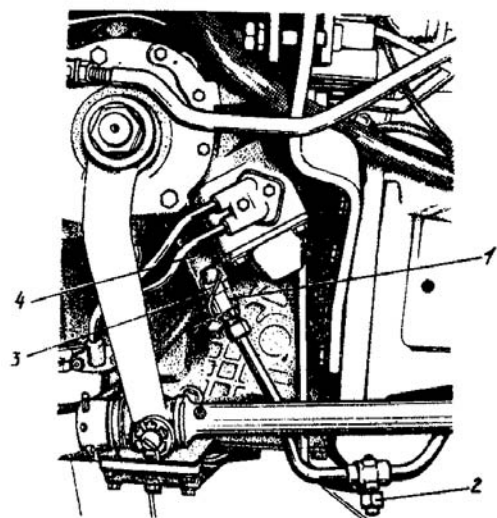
Подсоединение манометра к гидроусилителю: 1 — колпачок; 2 — штуцер; 3 — контргайка; 4 — предохранительный клапан
